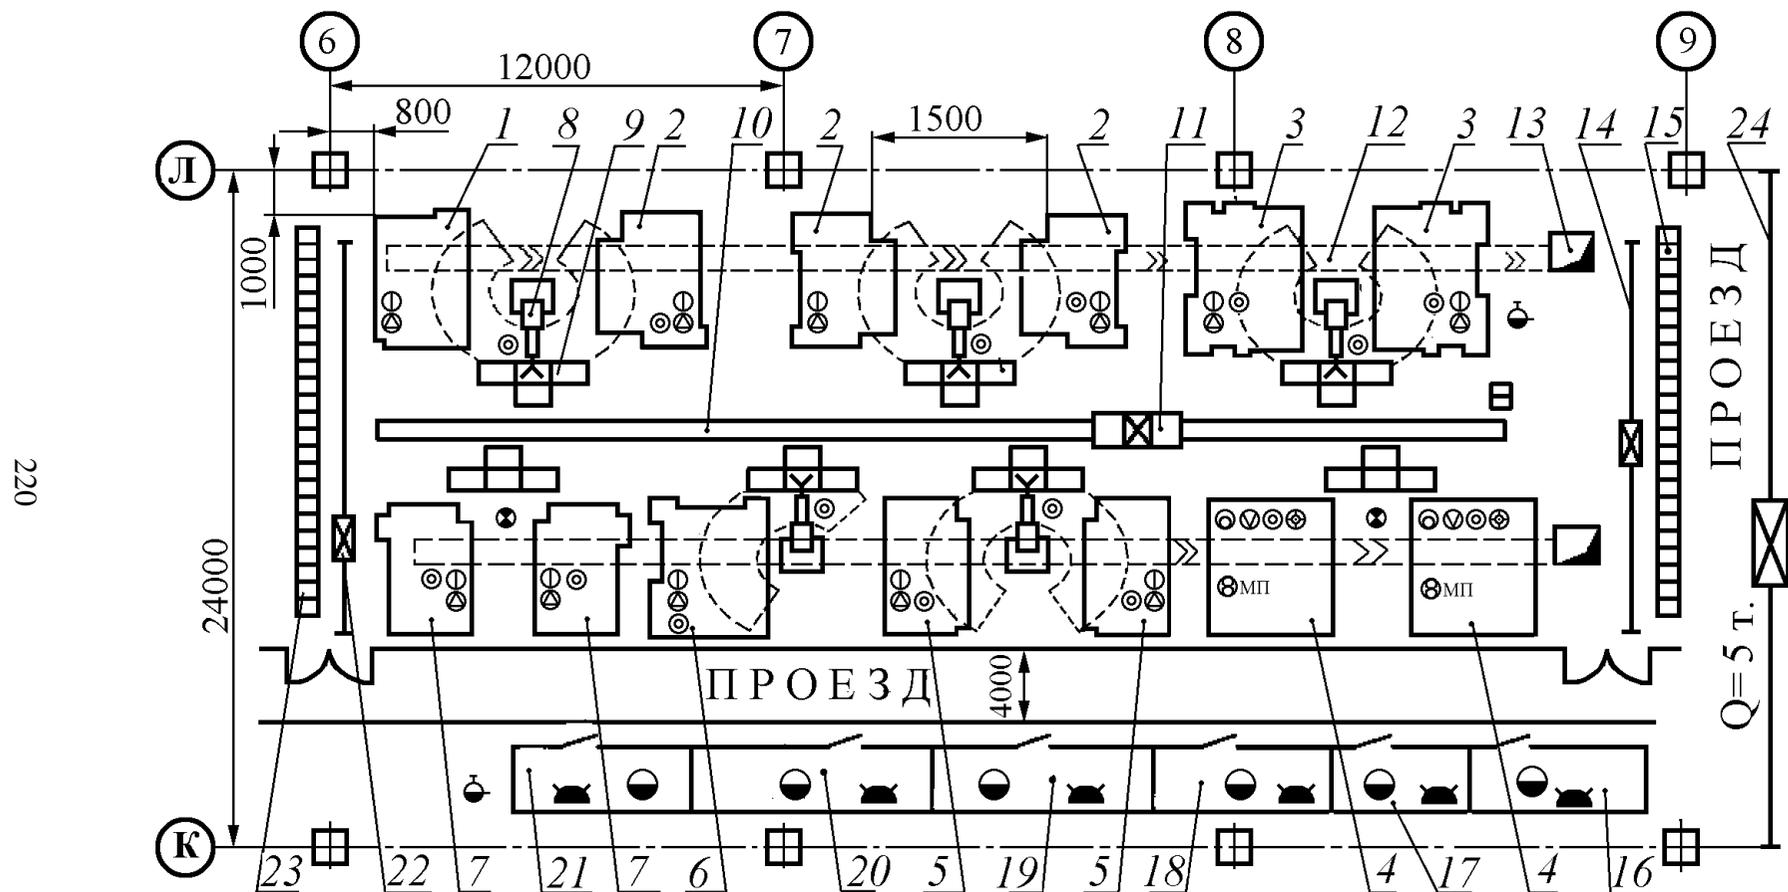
П14. Планировка участка по обработке корпусных деталей:
